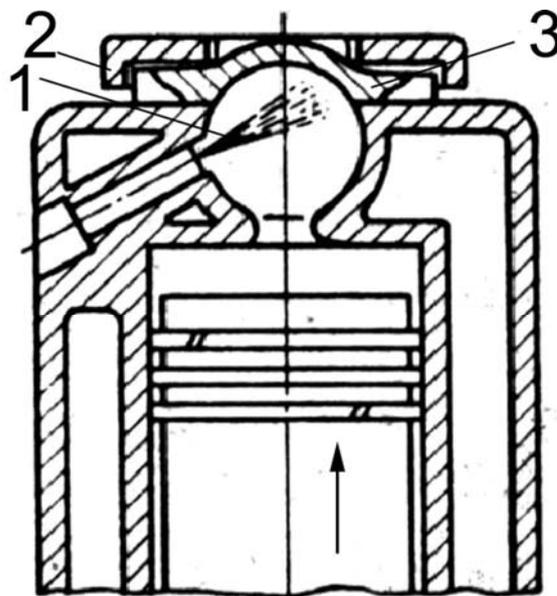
Схема калоризаторного двигателя. Обозначения: 1 – струя топлива, 2 – крышка головки цилиндра, 3 – калоризатор. Стрелкой показано направление движения поршня в момент подачи топлива
